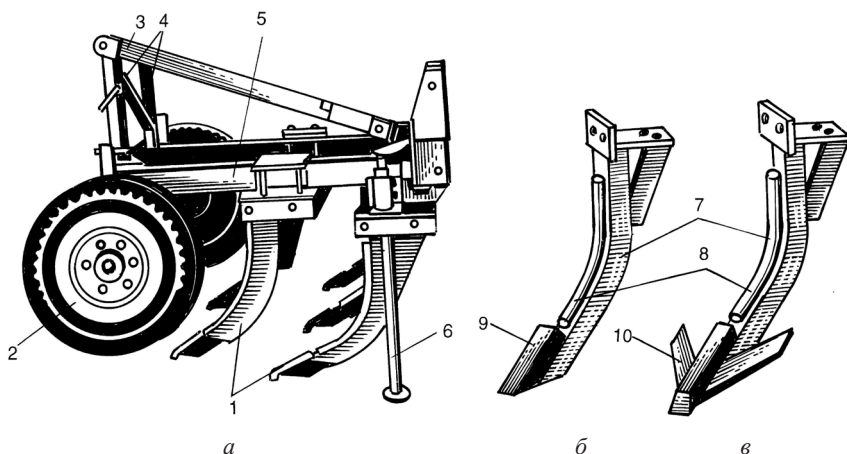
Чизельный плуг: а – общий вид; б, в – рабочие органы; 1 – рыхлители; 2 – опорное колесо; 3 – навесное устройство; 4 – регуляторы глубины обработки; 5 – рама; 6 – подставка; 7 – стойка; 8 – обтекатель; 9 – долото; 10 – стрелчатая лапа
